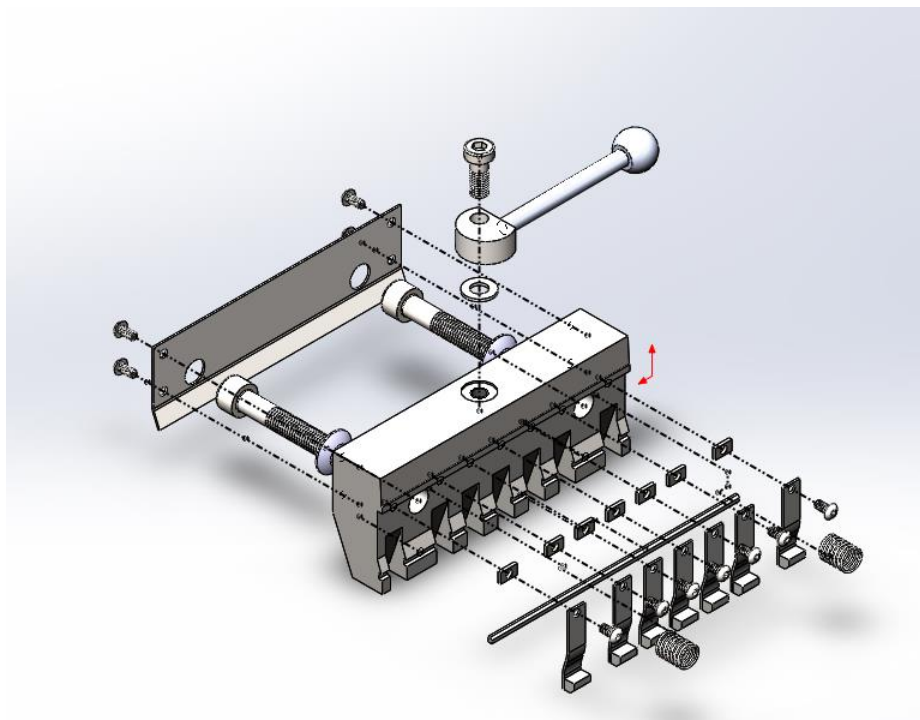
Vista explodida do Suporte_5 - Mola de lâmina
